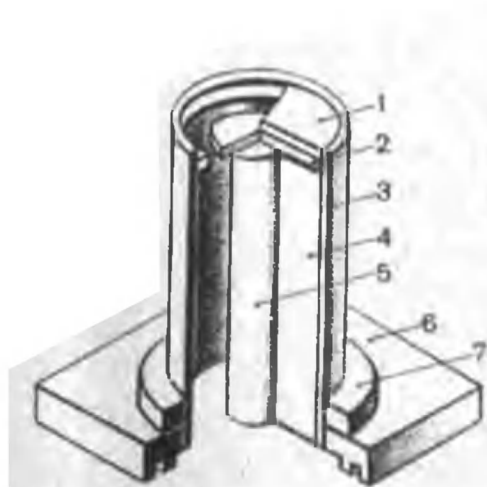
Приспособление для изготовления кругового фотометрического клина.
